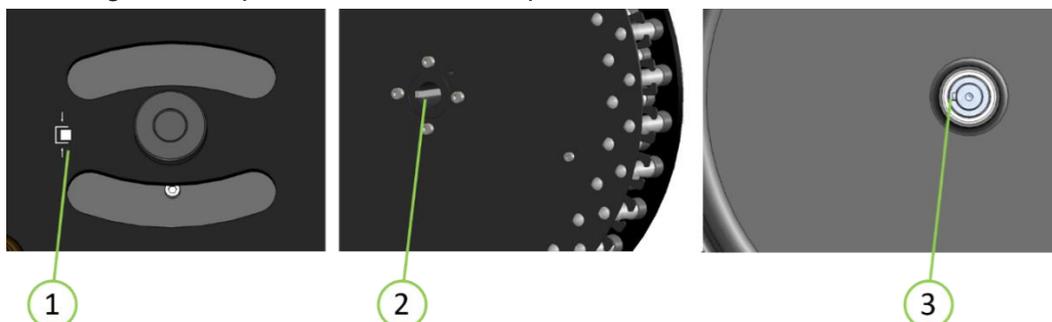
Gauche : Marquage sur le dessus du disque du rotor. Au milieu : Rainure vue du dessous du disque de rotor. A droite : Languette incluse dans l'axe du rotor visible après le retrait du disque de rotor.
